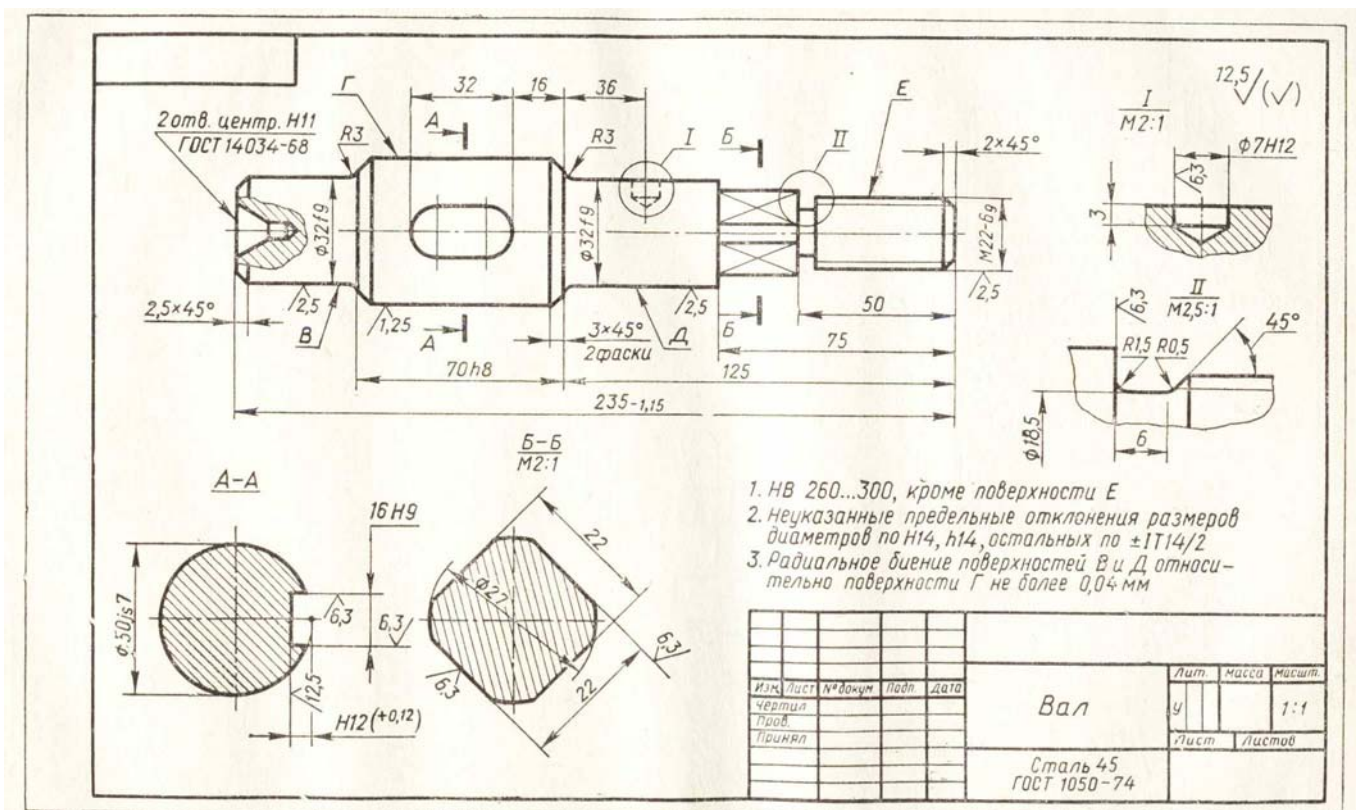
Чертеж вала с простановкой шероховатости поверхности
